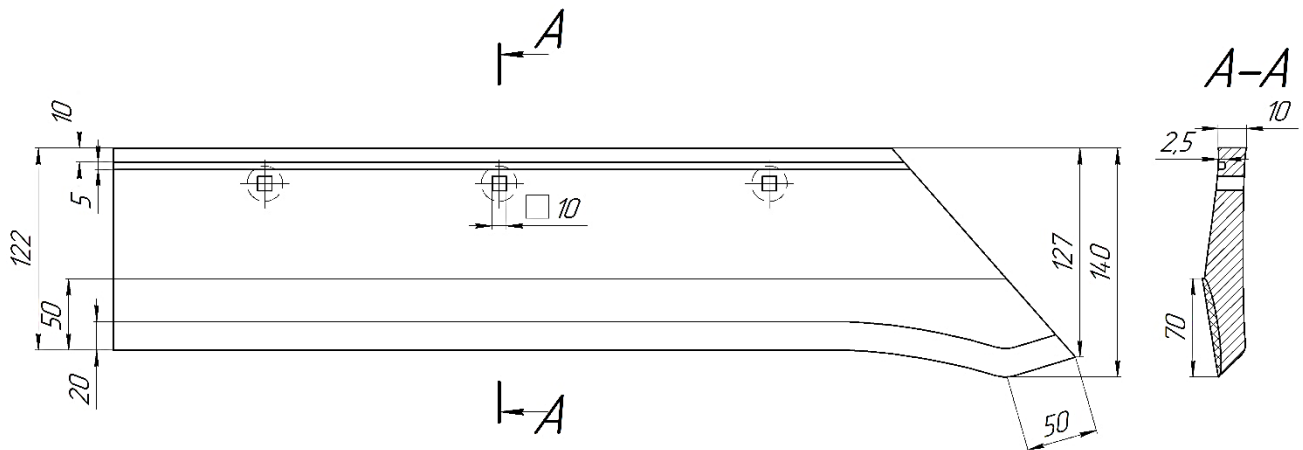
Конструкція та розміри лемеха типу ПНЧС 01.702
